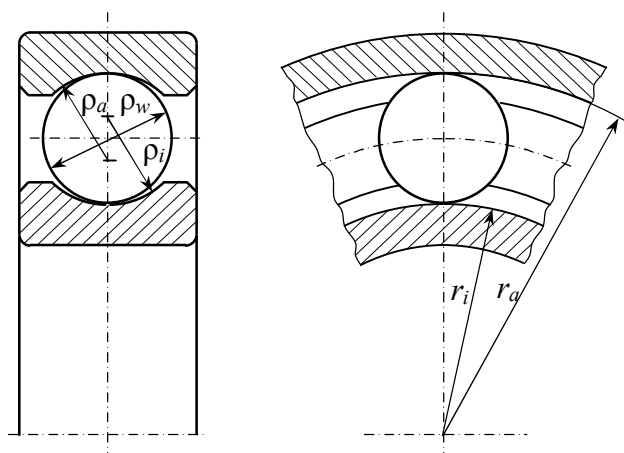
Размеры поверхностей контакта в шариковом подшипнике
